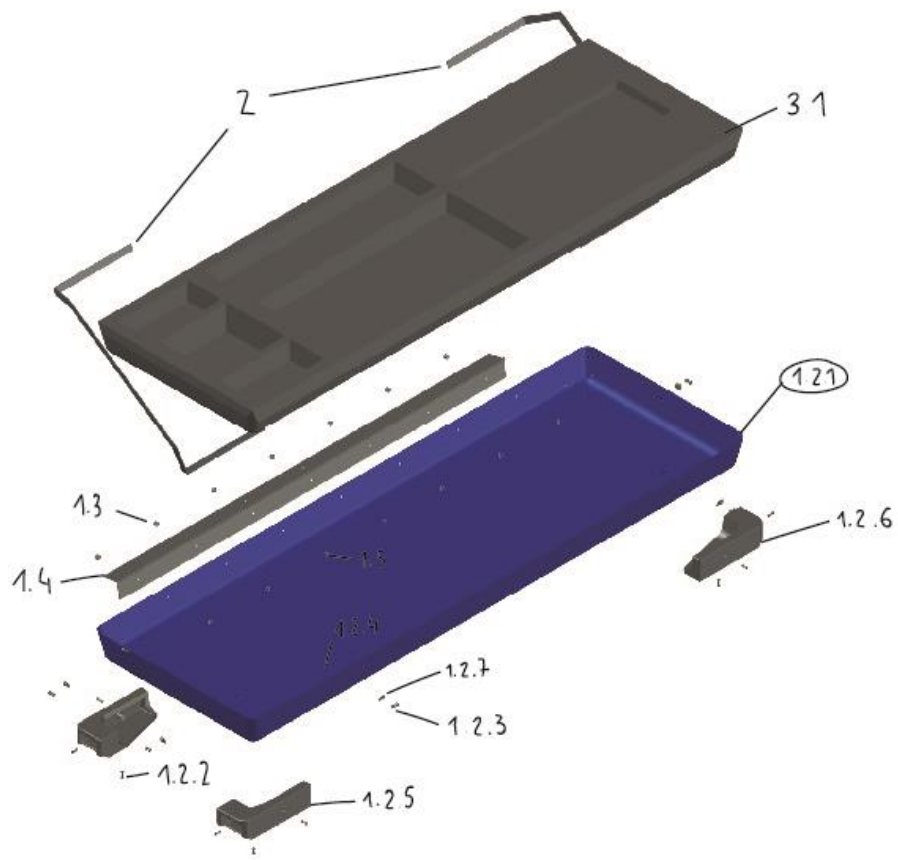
Explosionado de relaciones pieza 1.2.1
